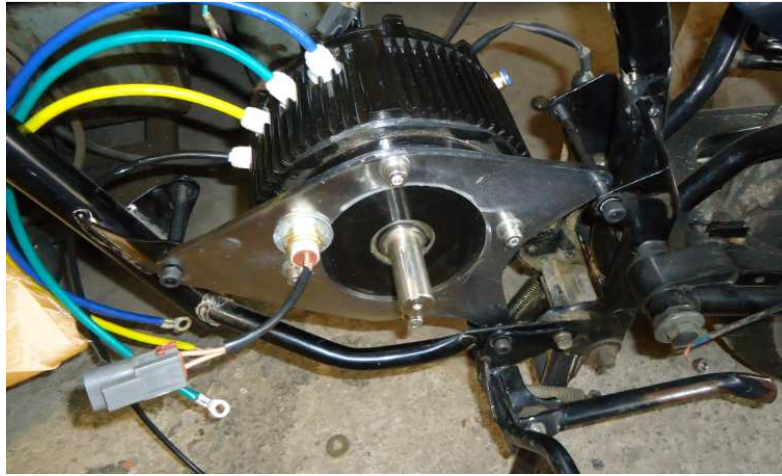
Comprobación geométrica de la placa soporte del motor.
